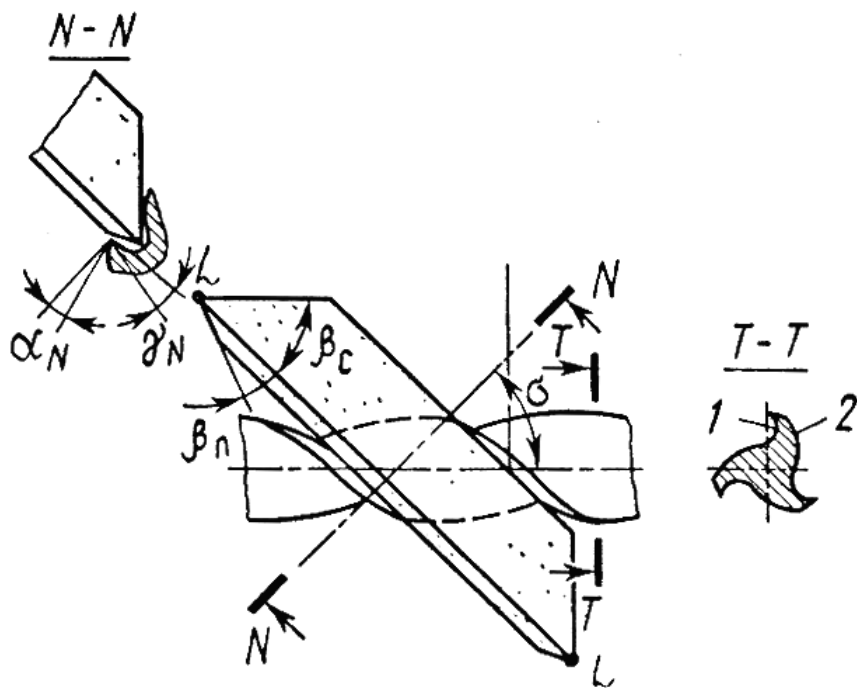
Схема расположения концевой фрезы и шлифовального круга при вышлифовке винтовых канавок:
